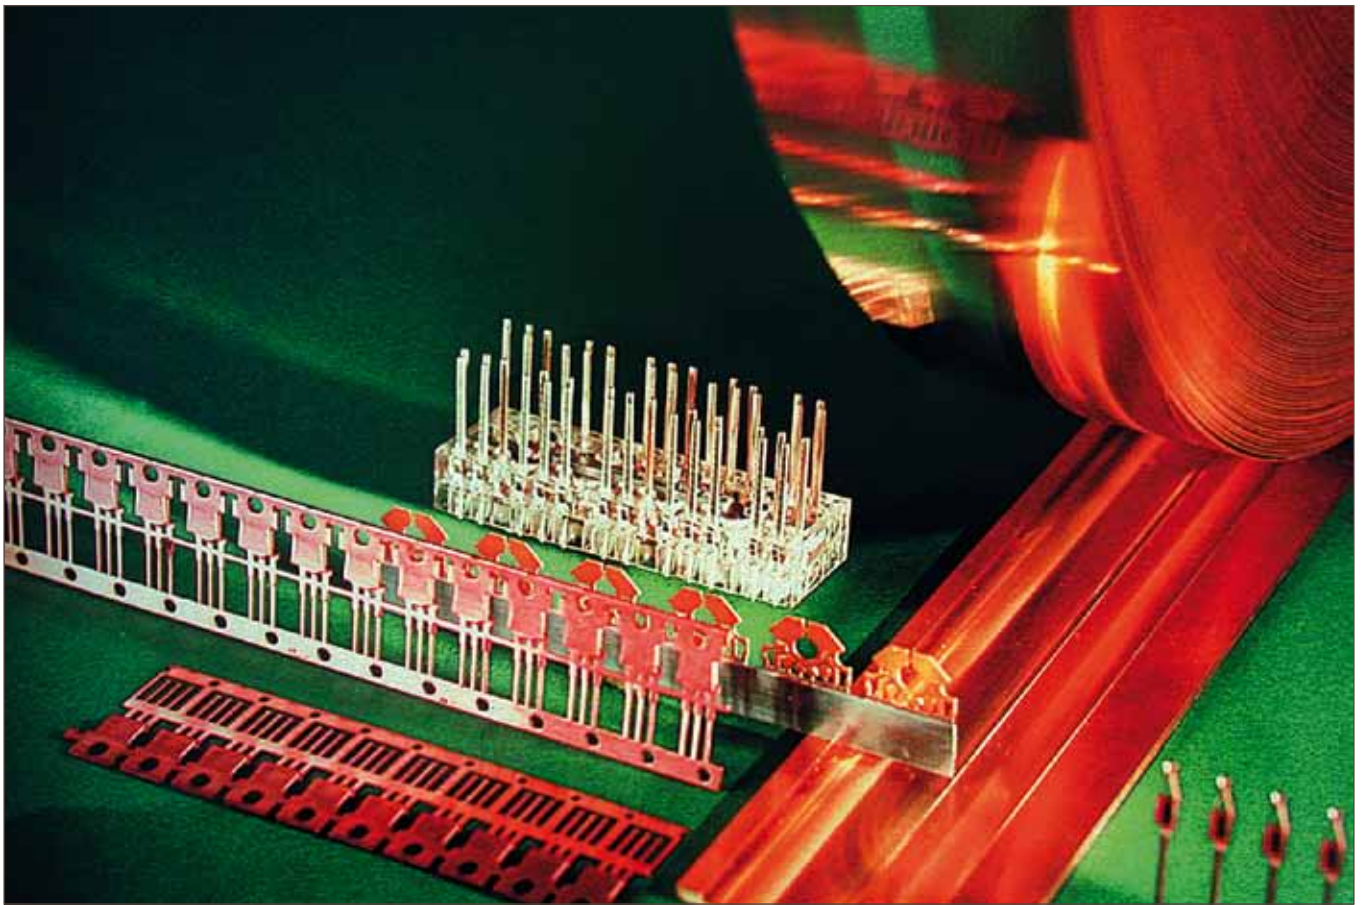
Bauelemente für die Elektrotechnik (DKI 6231)
